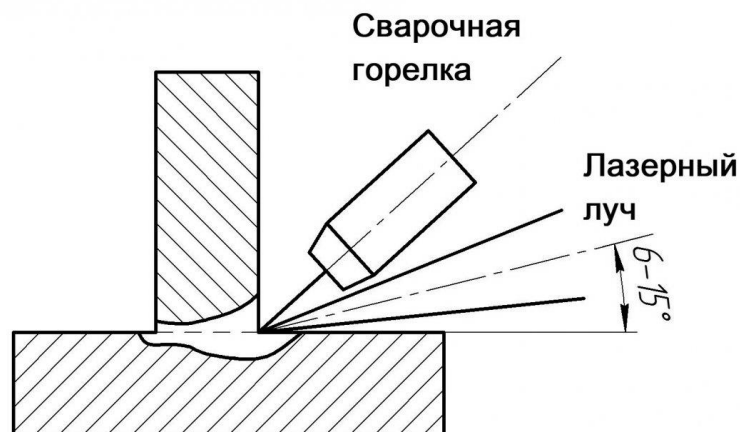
Схема гибридной лазерной сварки таврового сварного соединения
